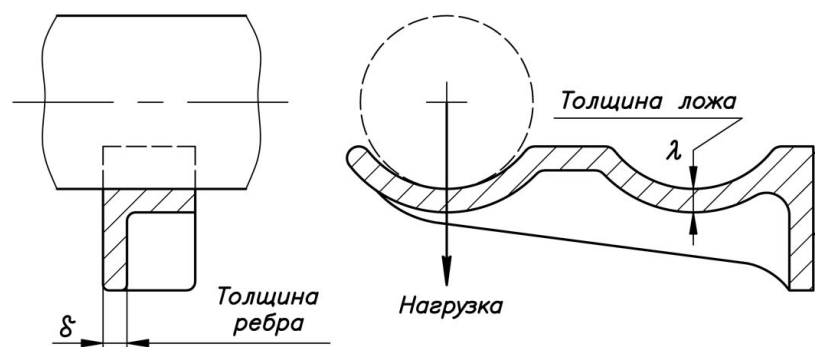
Форма и размеры поперечного сечения консоли ККЧ-2
